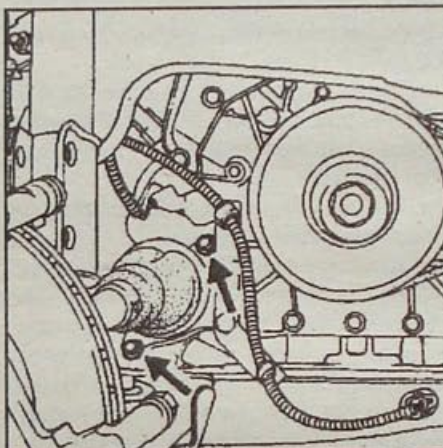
Расположение болтов крепления блокировочной пластины на промежуточной опоре
